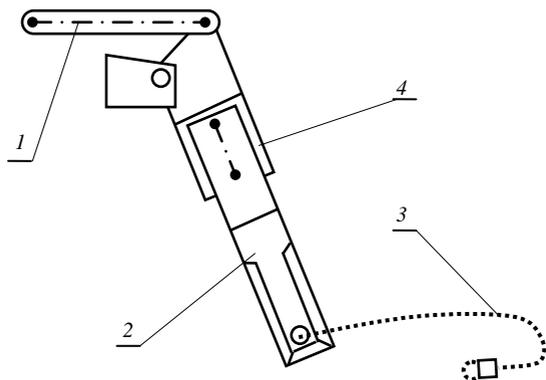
Конструкция присыпателя: 1 – тяга; 2 – нож; 3 – трос; 4 – щека
